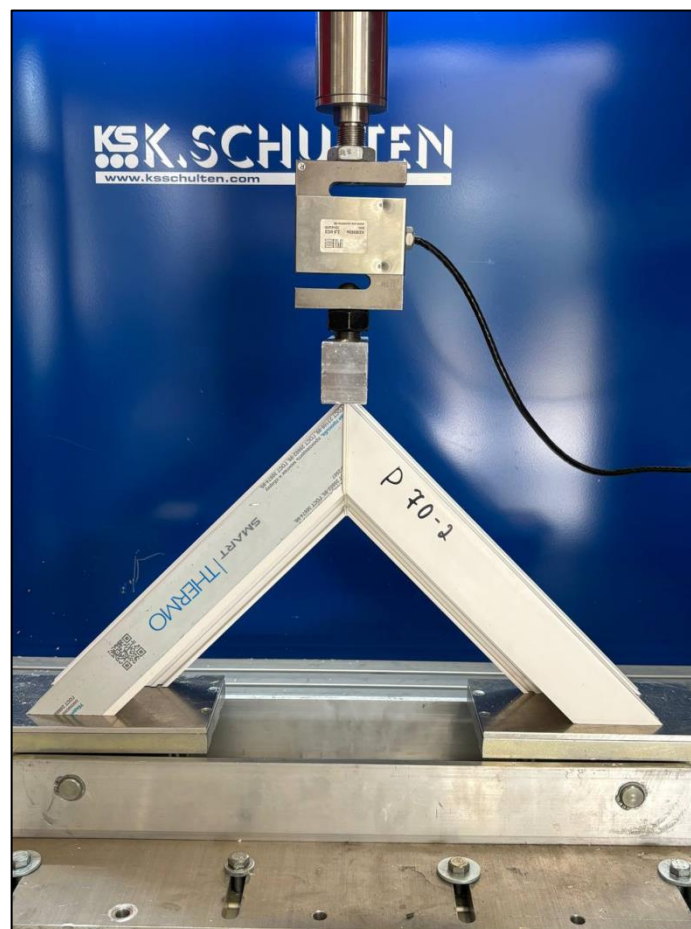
Испытуемый образец 666-24/5, установленный на испытательный стенд
